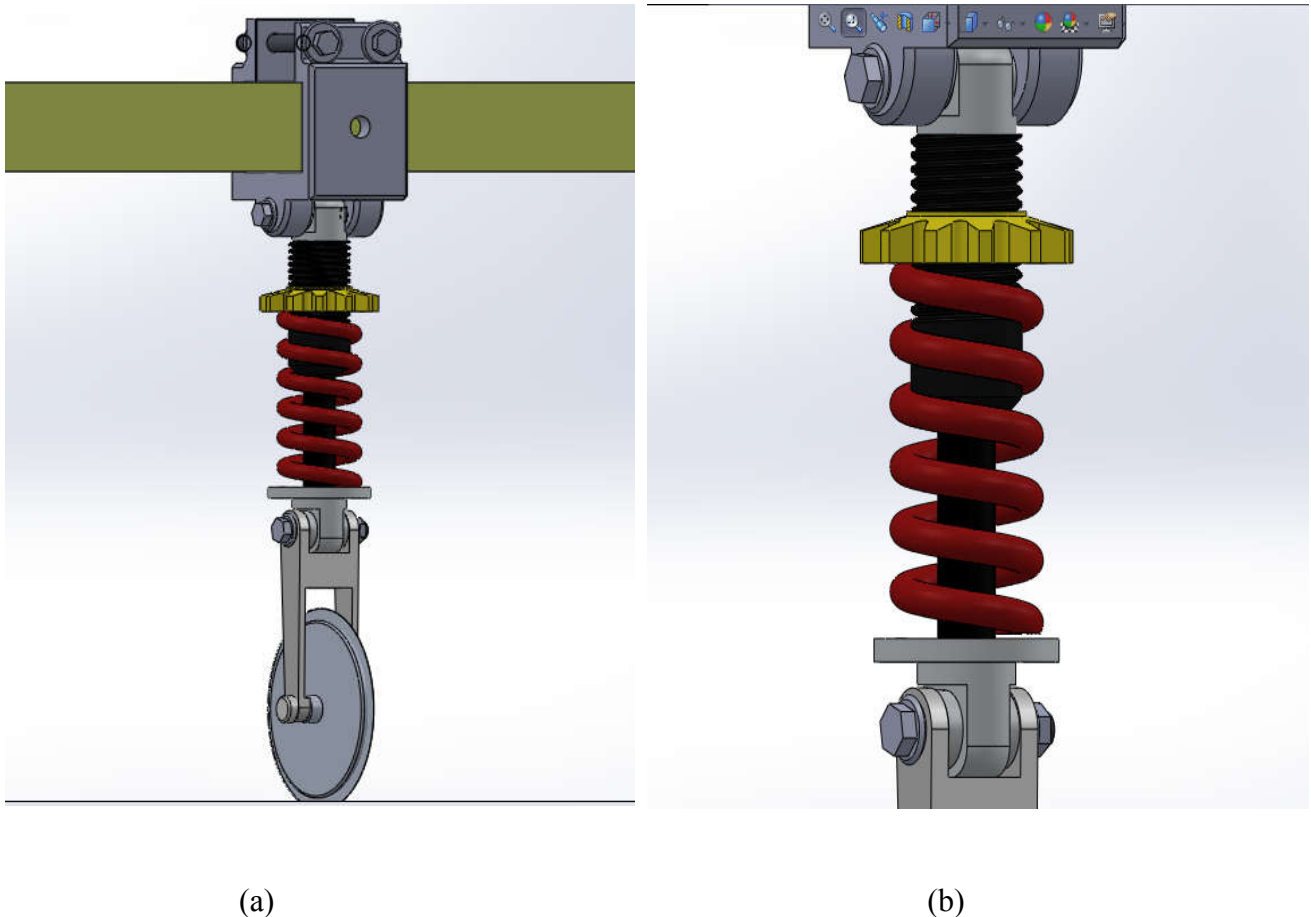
sous assemblage de roues de coupe : (a) assemblage du ressort de suspension avec la tige en acier (b) assemblage de la roue de coupe rotative avec la tige.
